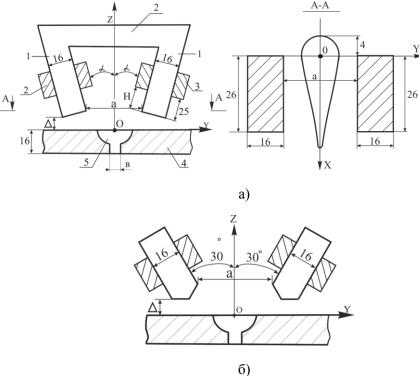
Схем размещения УВ ПОМП: 1-стержни; 2-перемычка; 3- обмотки (катушки); 4- пластины; 5- полость сварочной ванны.
